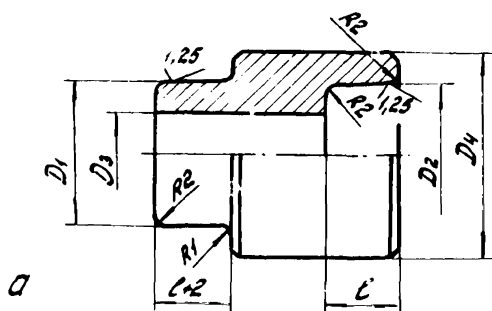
Схема нагревательного инструмента для раструбно-стыковой сварки:
